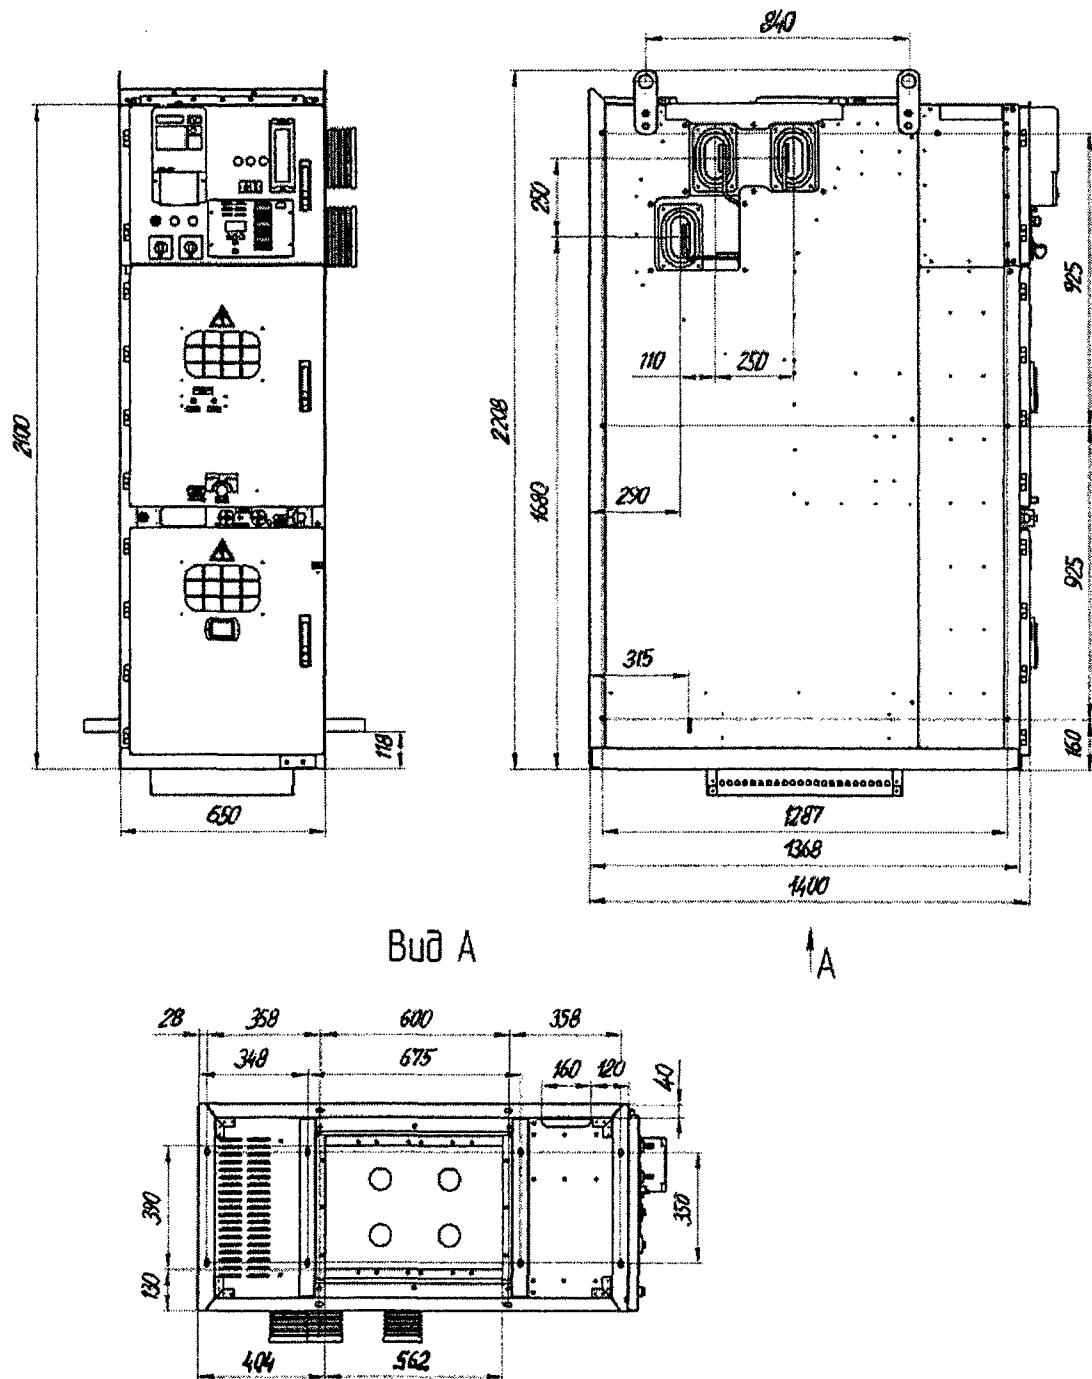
Габаритные и присоединительные размеры шкафа КРУ «ТЕМЗА» на номинальный ток 630-1600 А
